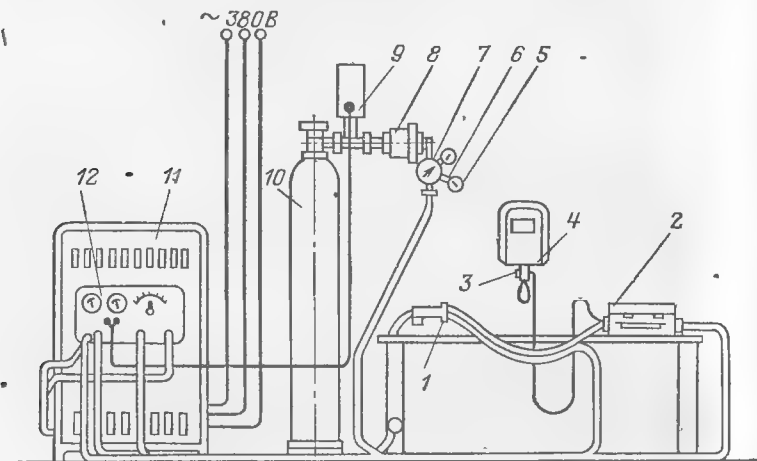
Схема поста А-547Р для полуавтоматической сварки в среде углекислого газа.
